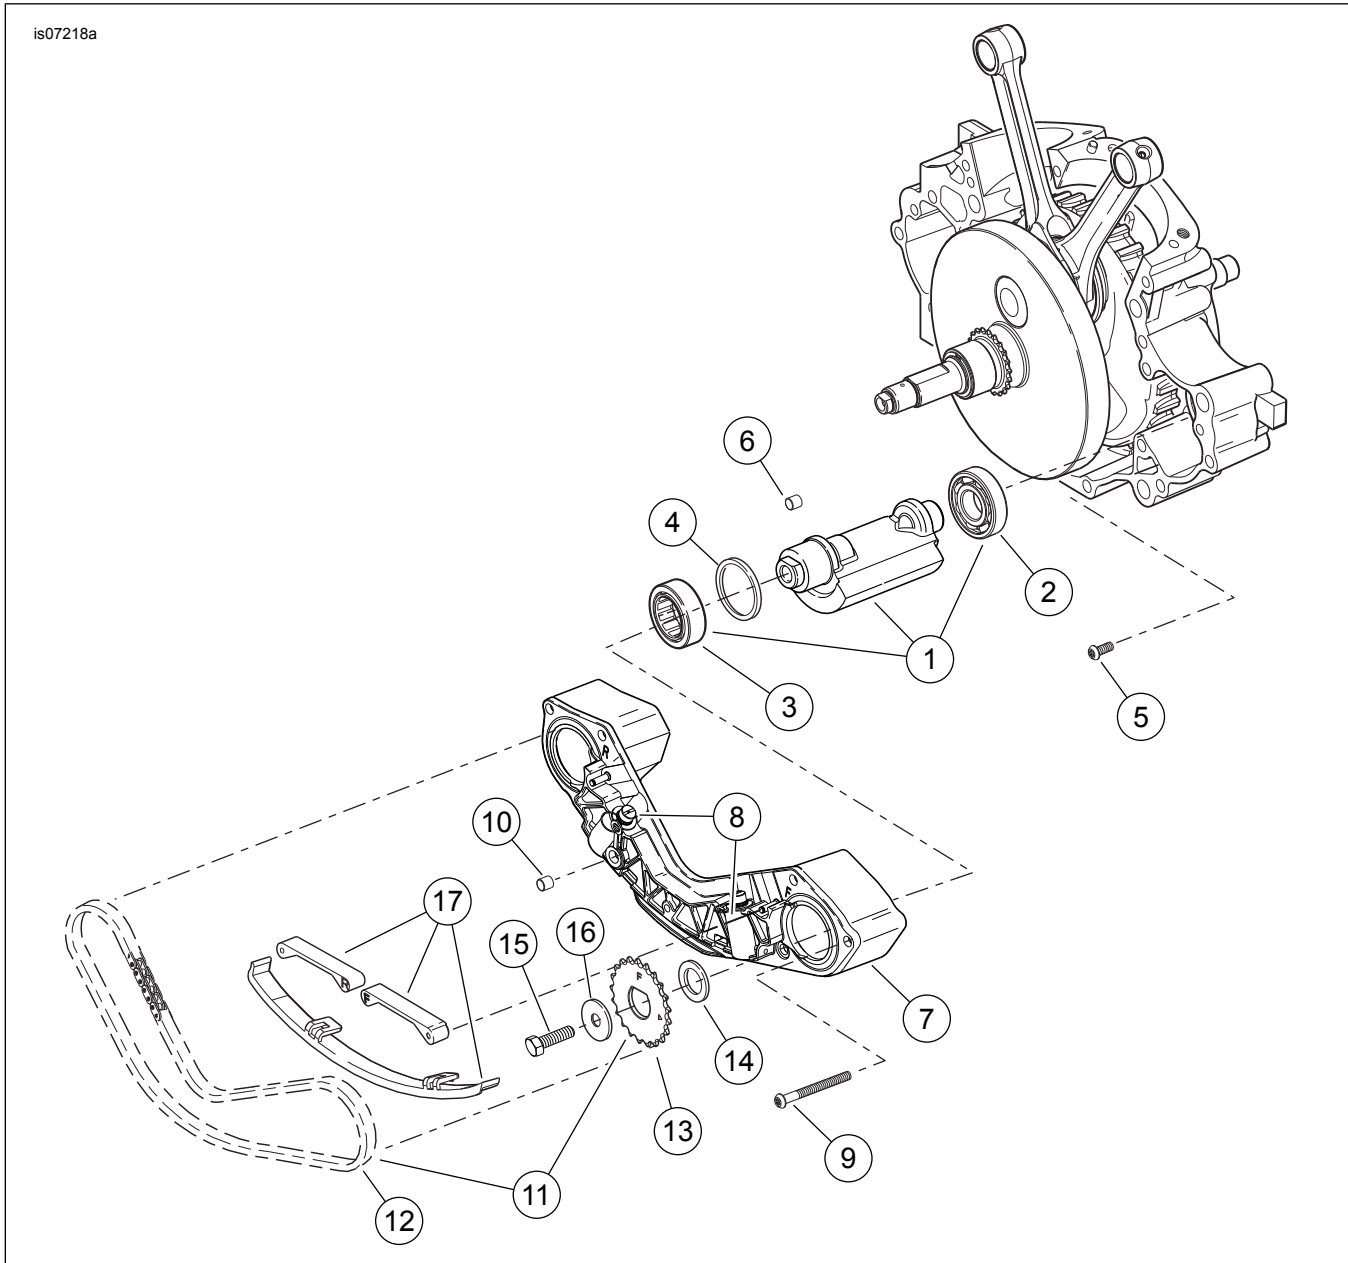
Piezas de servicio: SE120R Screamin' Eagle Pro Crate Engine (Beta) Equilibrador de motor
